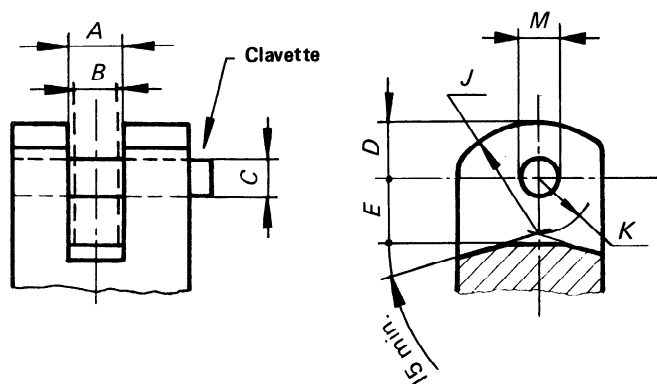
Chape d'ancrage — Schéma d'encombrement
